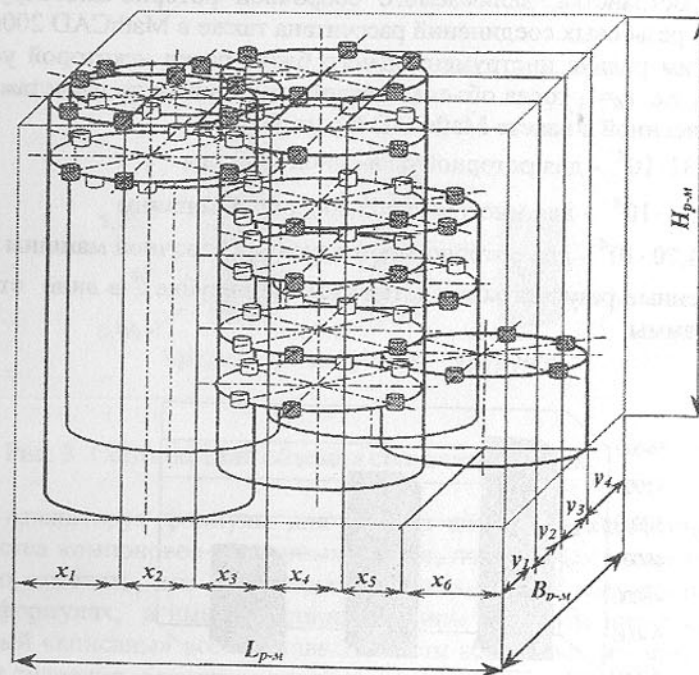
Модель компоновки роторно-многоярусной сборочной машины для резьбового соединения
